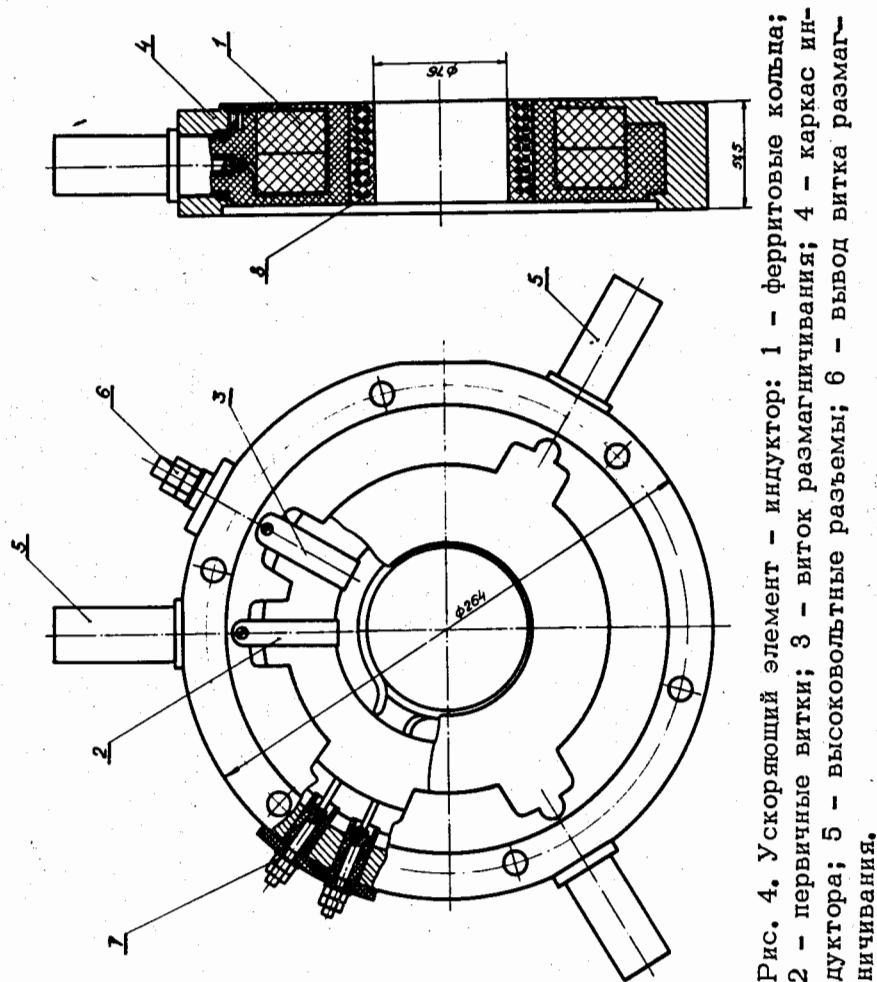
Ускоряющий элемент - индуктор: 1 - ферритовые кольца; 2 - первичные витки; 3 - виток размагничивания; 4 - каркас индуктора; 5 - высоковольтные разъемы; 6 - вывод витка размагничивания.
